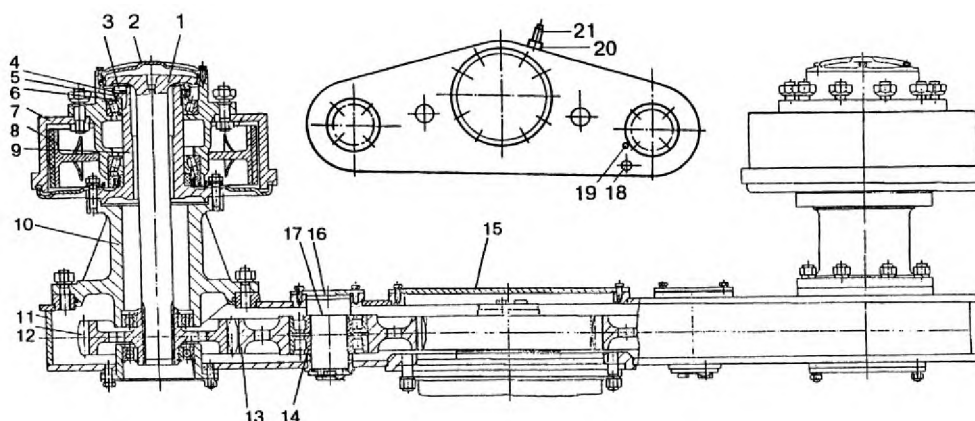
Балансир автогрейдера А120: 1 – полуось; 2 – крышка ступицы колеса; 3 – контргайка подшипников колеса; 4 – замочная шайба; 5 – гайка подшипников колеса; 6 – конический подшипник; 7 – ступица с тормозным барабаном; 8 – тормоз; 9 – цапфа; 10 – корпус; 11 – корпус редуктора; 12, 13 – шестерни; 14 – подшипник; 15, 16 – крышки; 17 – ось; 18 – магнитная пробка сливного отверстия; 19 – коническая пробка контрольного отверстия; 20 – пробка заливного отверстия; 21 – сапун
